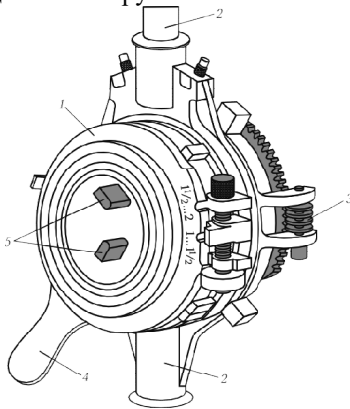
Клуп для нарізування трубних різьблень: 1 – корпус; 2 – рукоятки; 3 – черв'ячна передача; 4 – рукоятка переміщення плашок; 5 – плашки
